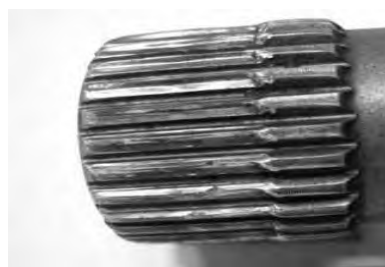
Срезание шлицев втулки турбинного колеса трансформатора и первичного вала коробки передач
